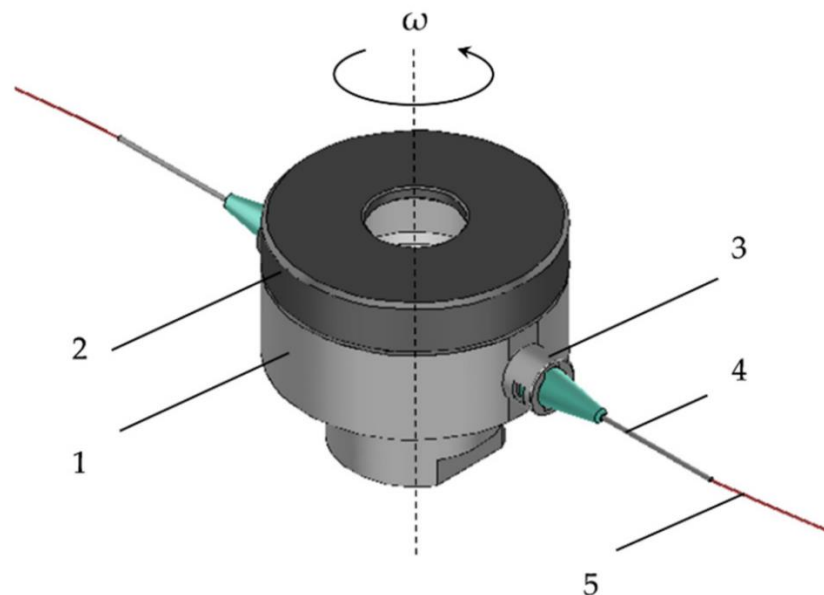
Спеціально розроблена відцентрова обертальна головка: 1 – нижня частина; 2 – ковпачок; 3 – з'єднувач різьби до приманки; 4 – голка та 5 – полімерний розплав [89].
